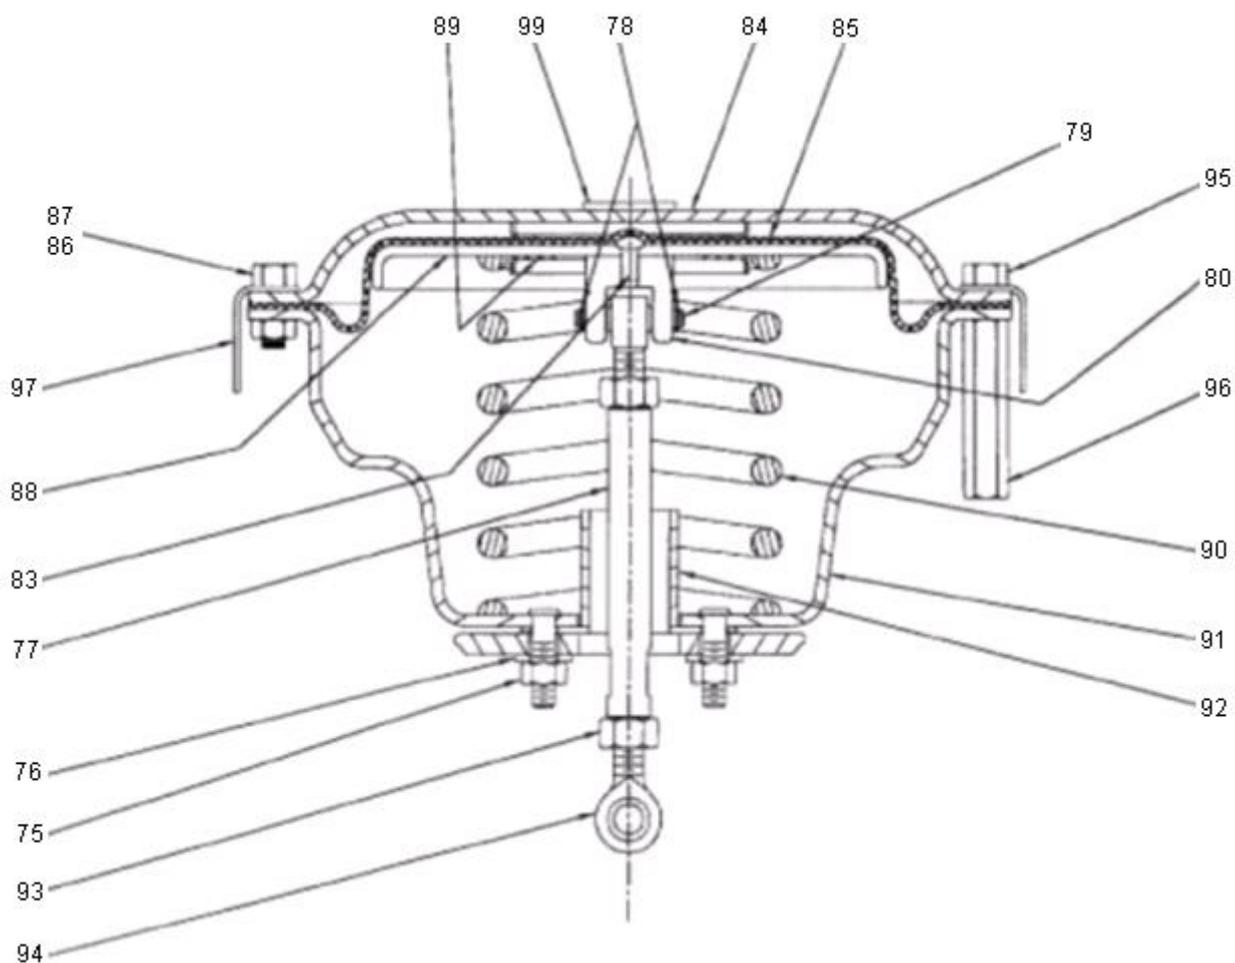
Общий вид привода в сборе. Размеры В и С
